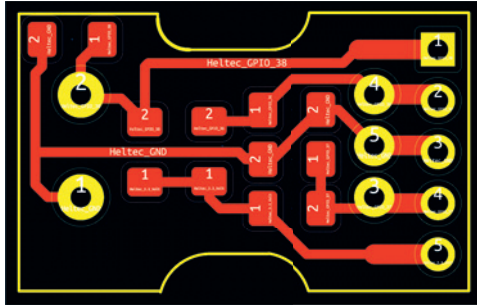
Platinenlayout für die Zusatzschaltung für den Drehkoder.
